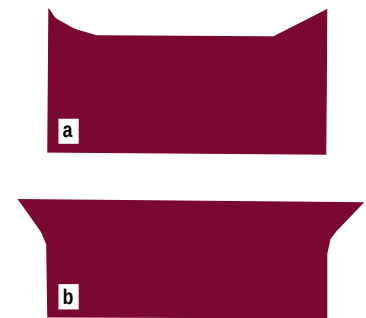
Schlichtung des Formlings, Querschnitt
